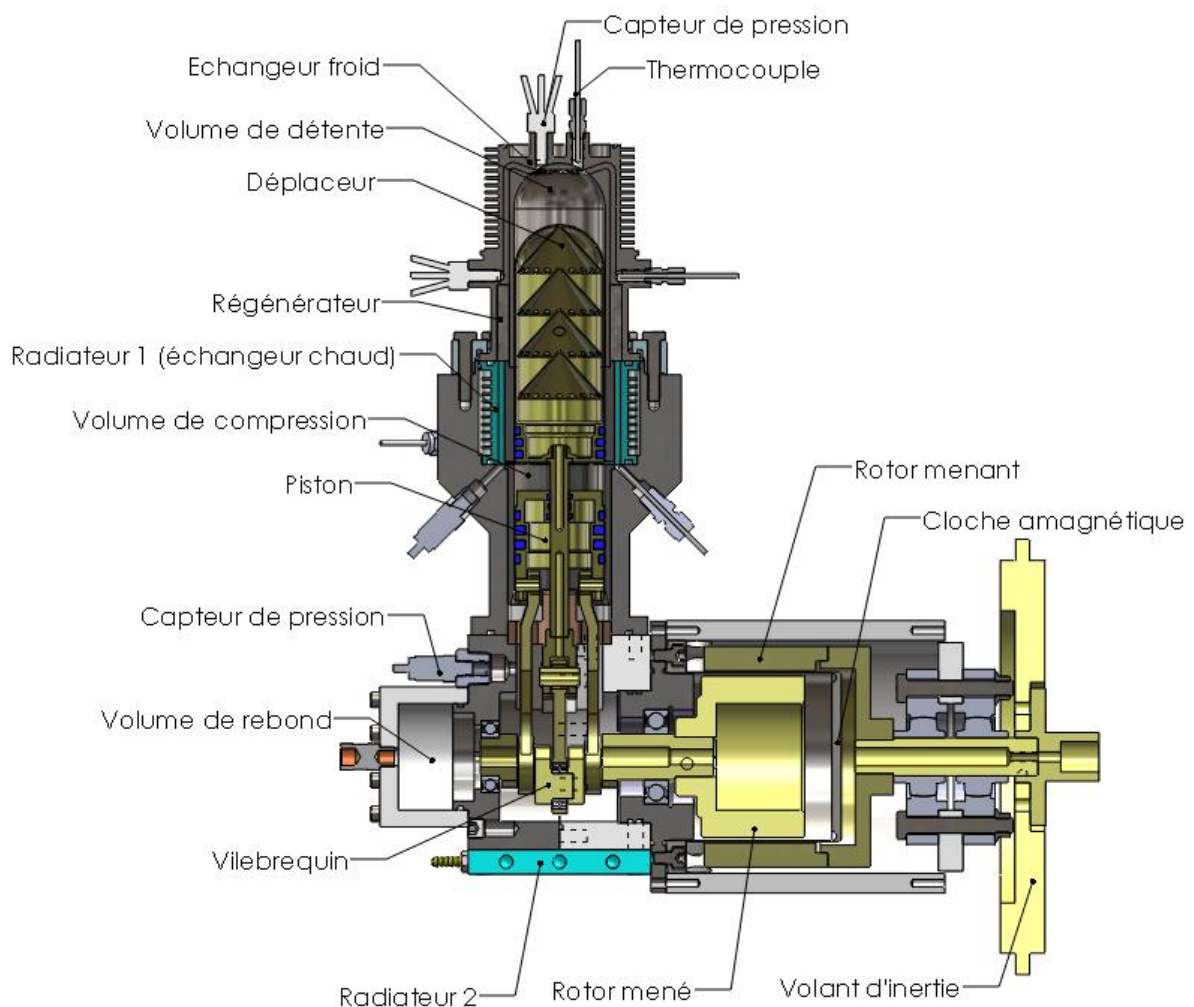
vue en coupe de la machine réceptrice de Stirling pour la production du froid.
